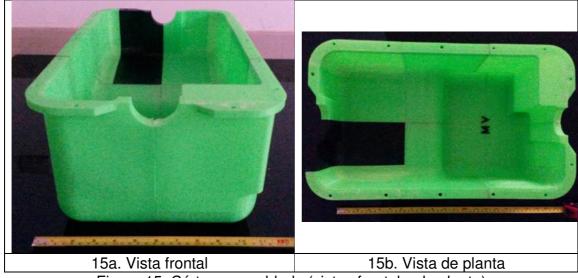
Cárter ensamblado (vistas frontal y de planta)
